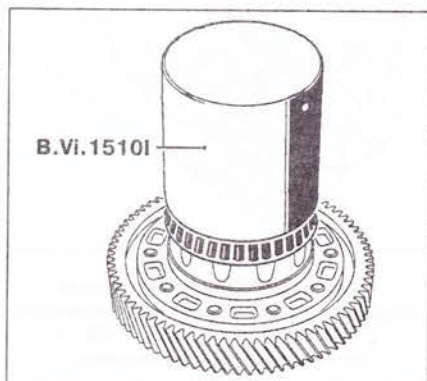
Установите большой подшипник при помощи приспособления В. Vi. 1510I.
